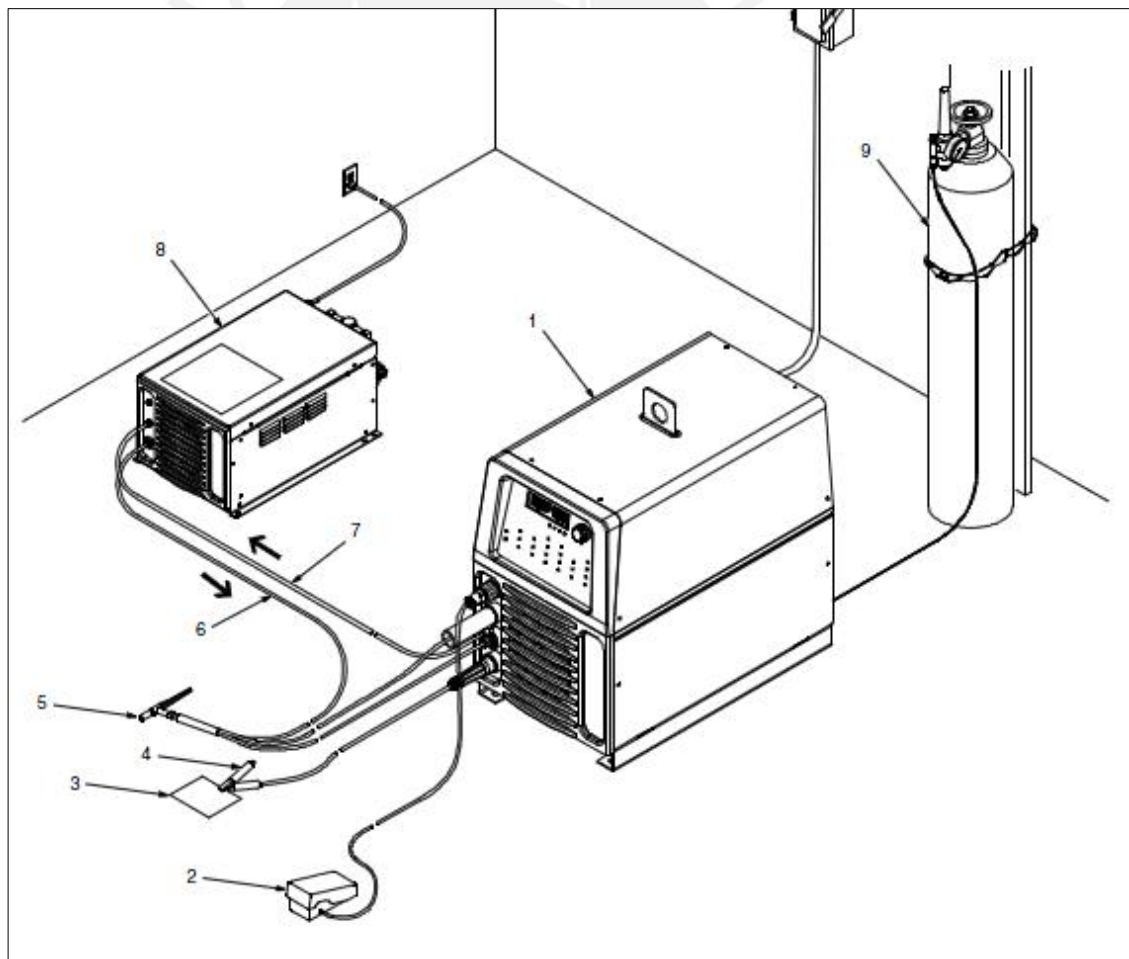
Equipo necesario para el proceso de soldadura GTAW [5]
